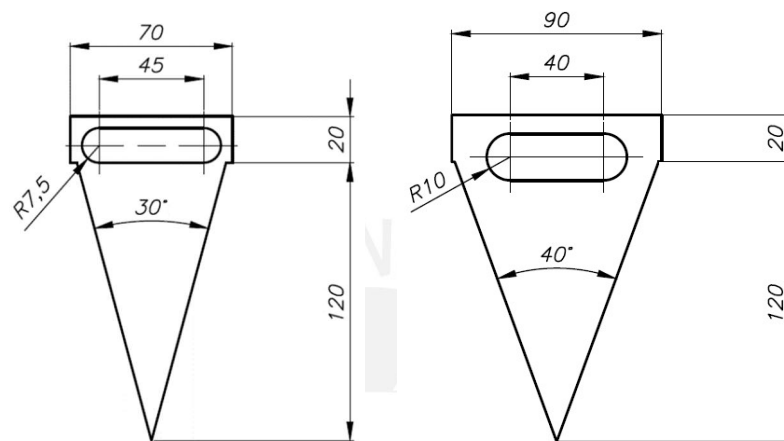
3. Dimensiones de la cuchilla de 30° (izquierda) y de 40° (derecha)
